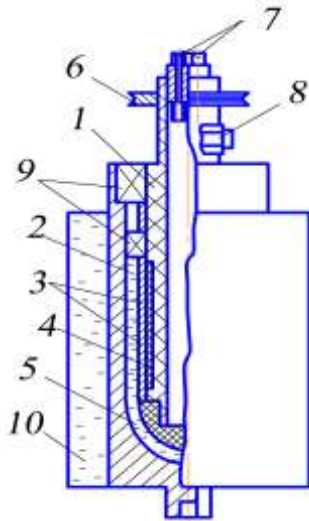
Конструкция измерительного устройства: 1 – внутренний цилиндр; 2 – наружный цилиндр; 3 – нагреватель; 4 – гильза; 5 – нижний торец; 6 – шкив; 7 – спираль; 8 – разъем; 9 – подшипник; 10 – водяная рубашка
